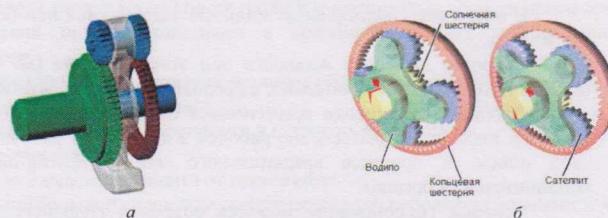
а) многоступенчатый редуктор, б) планетарный редуктор
